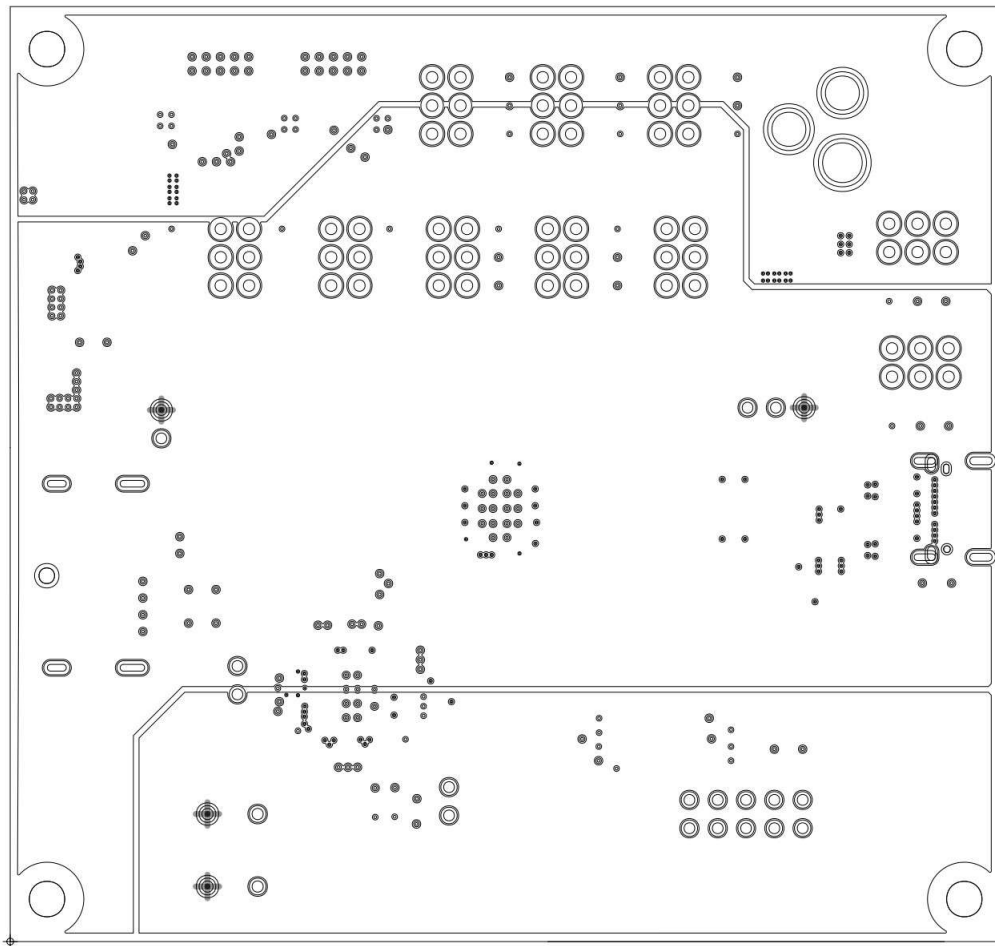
TUSB5461-Q1 EVM PCB 第 3 层 (电源)
